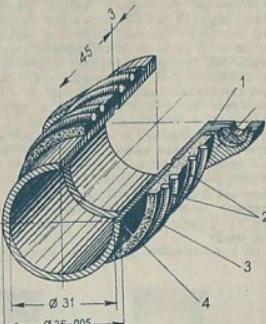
Патрубок смягчающий вибрации карбюратора 1 и стандартный патрубок крепления карбюратора 2; хомуты (из проволоки); 3 — дюритовый шланг; 4 — втулка (самодельная).
